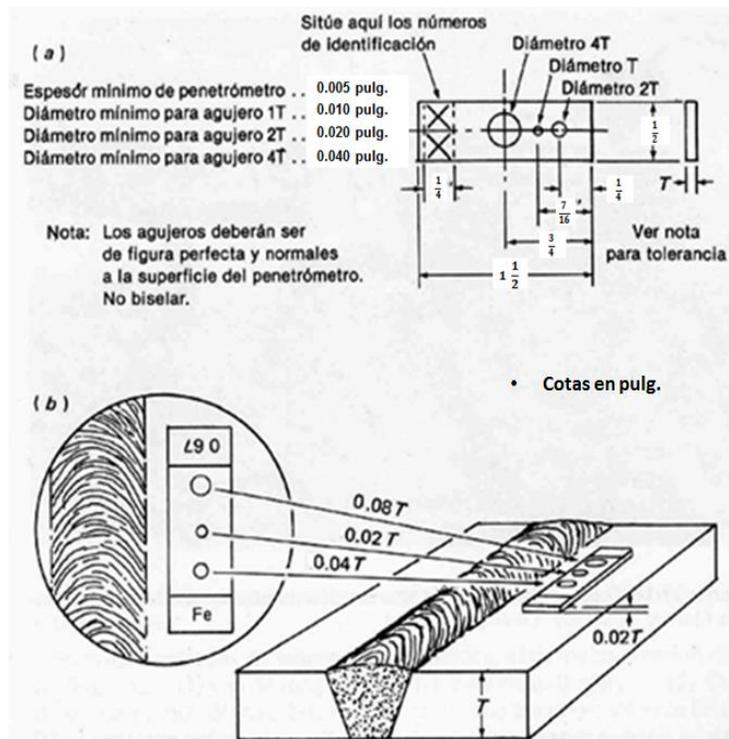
Penetrómetro, al lado de la soldadura y alejado de la película: (a) Diseño de penetrómetro para espesores de 0.005 a 0.050 pulg, y (b) colocación del penetrómetro.
